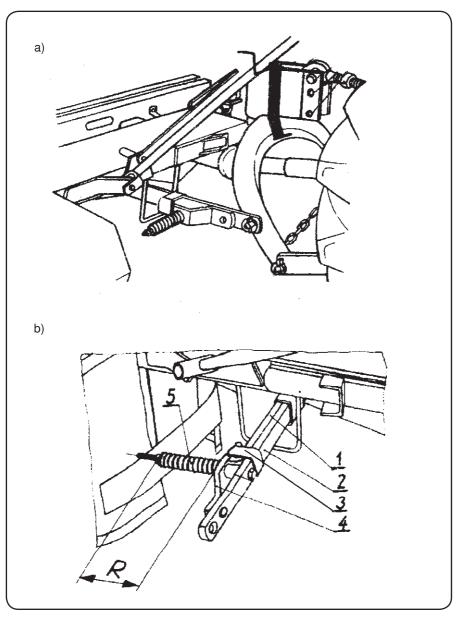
Предохранитель косилки Z -178 в положениях: а-рабочем, б- транпортном.
